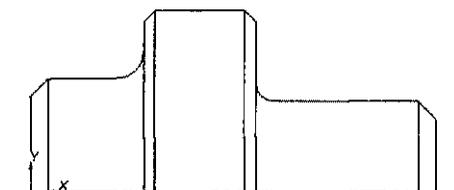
Прототип верхней части детали с фасками и скруглениями
